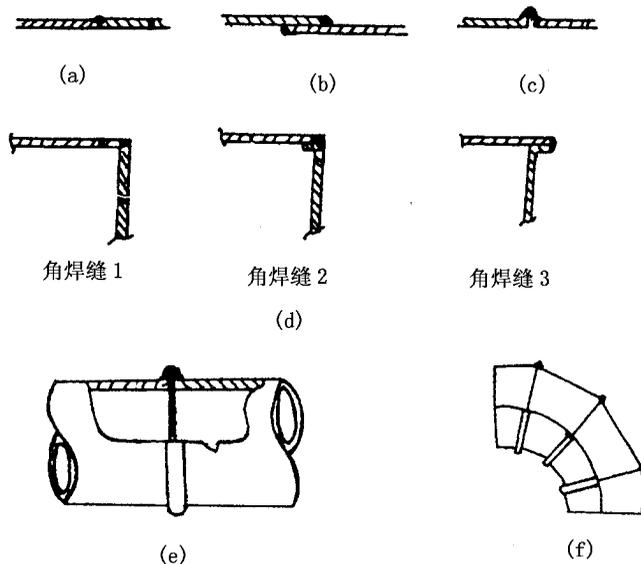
钢板焊缝型式及翻边焊示意图
